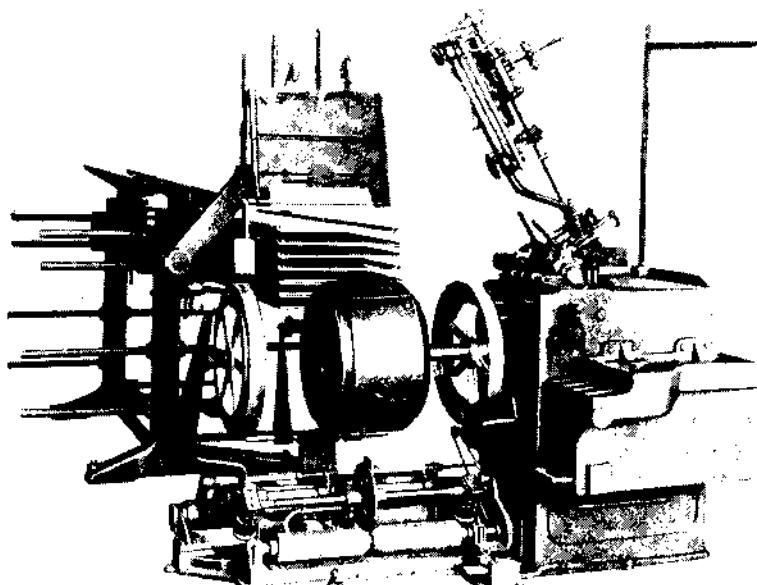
Станок для изготовления покрышек полуплоским способом.
